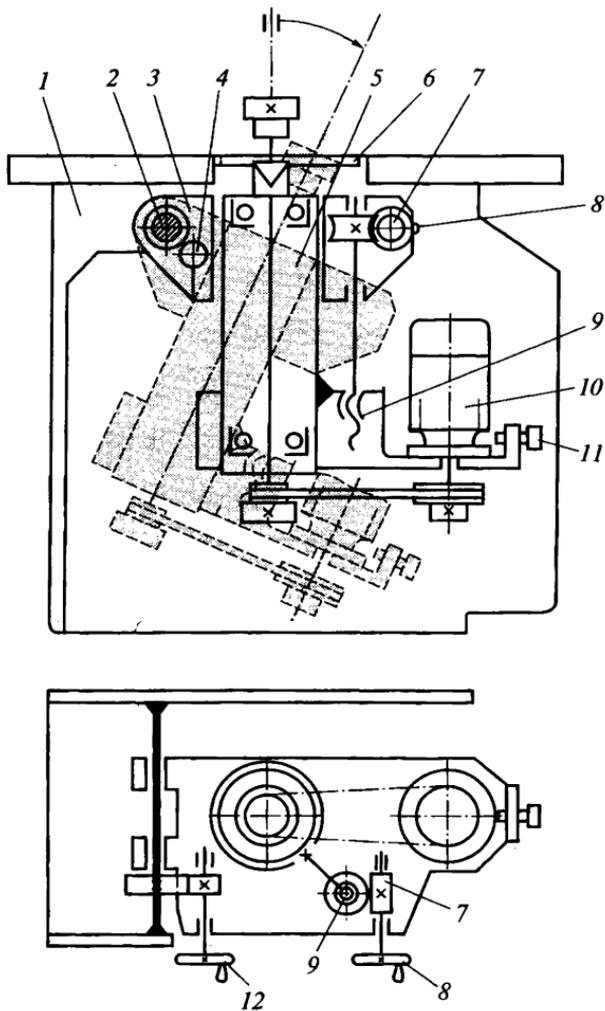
Фрезерный станок с наклоняемым суппортом:
